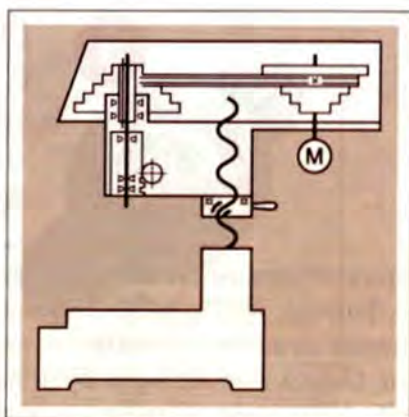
, а. Вертикально-свердлильний настільний верстат 2М112:
